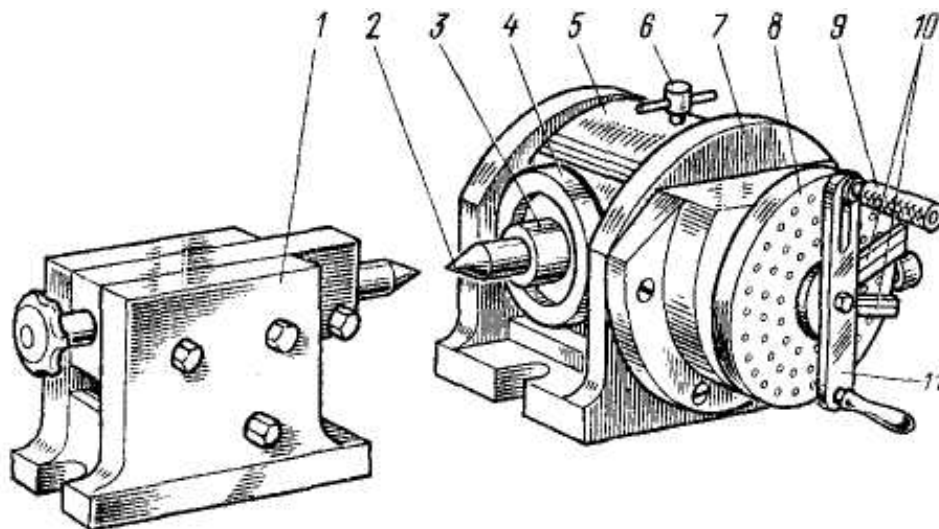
Универсальная делительная головка: 1 – задний центр; 2 – центр головки; 3 – шпиндель; 4 – диск непосредственного деления; 5 – корпус; 6 – стопор; 7 – основание; 8 – делительный диск; 9 – фиксатор; 10 – раздвижной сектор; 11 – рукоятка
